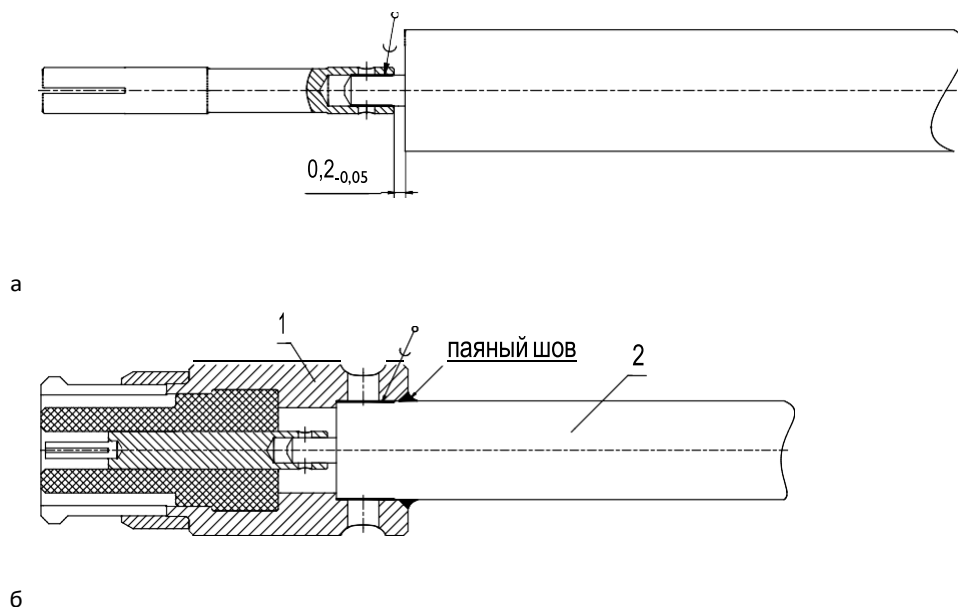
Пайка гнезда на жилу (а) и установка корпуса на кабель (б)
